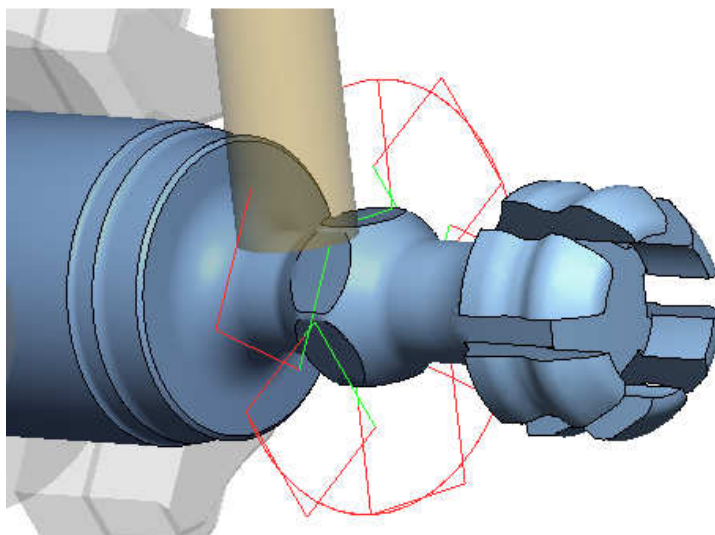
Vyhrubovanie a dokončenie hlavy veže
